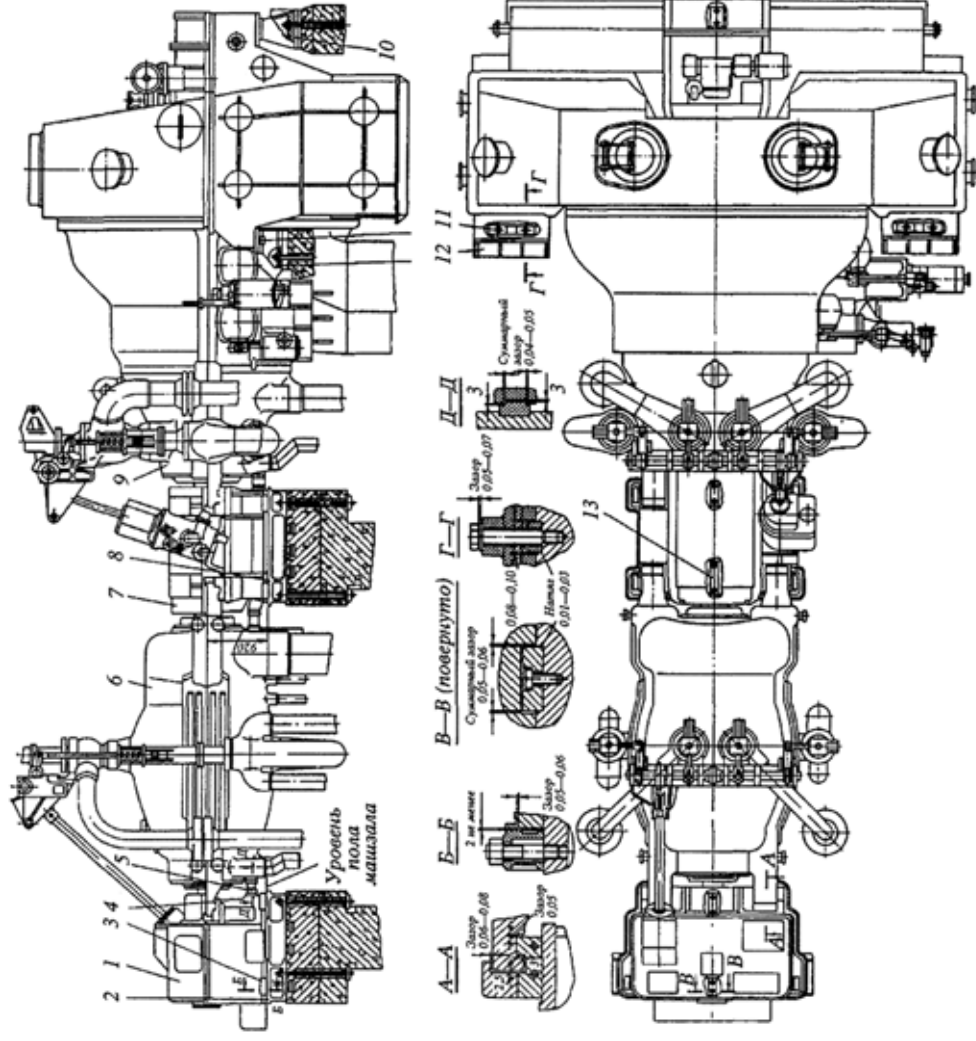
Установка турбины ПТ-135/165-130 ТМЗ на фундаменте: 1 – корпус переднего подшипника; 2 – фундаментная рама переднего подшипника; 3 – зажим «Г-образный»; 4 – шпонка поперечная; 5 – шпонка вертикальная; 6 – цилиндр высокого давления; 7 – корпус второго и третьего подшипников; 8 – фундаментная рама корпуса второго и третьего подшипников; 9 – цилиндр низкого давления; 10 – фундаментная рама задняя; 11 – шпонка поперечная (фикспункт); 12 – фундаментная рама боковая; 13 – шпонка продольная
